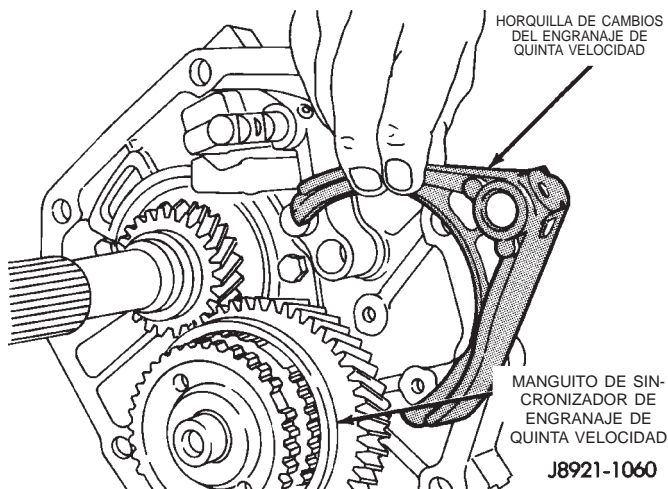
Instalación de horquilla de cambio del engranaje de quinta velocidad
